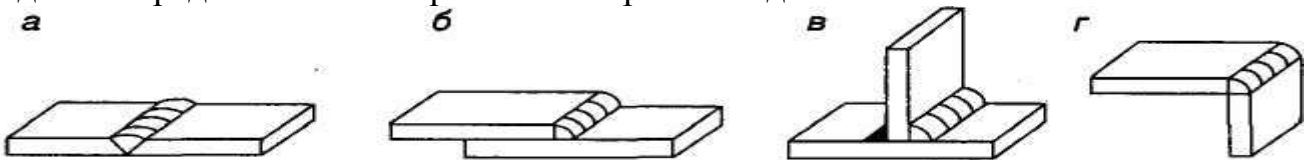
Типы сварных соединений: а — стыковое; б — нахлесточное; в — тавровое; г — угловое
